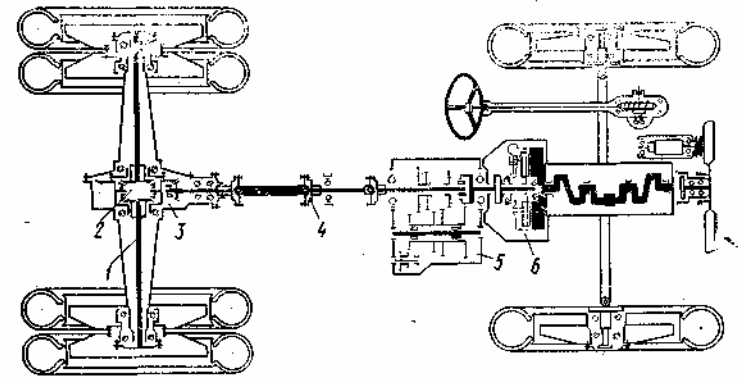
Схема силовой передачи двухосного автомобиля с задней ведущей осью
